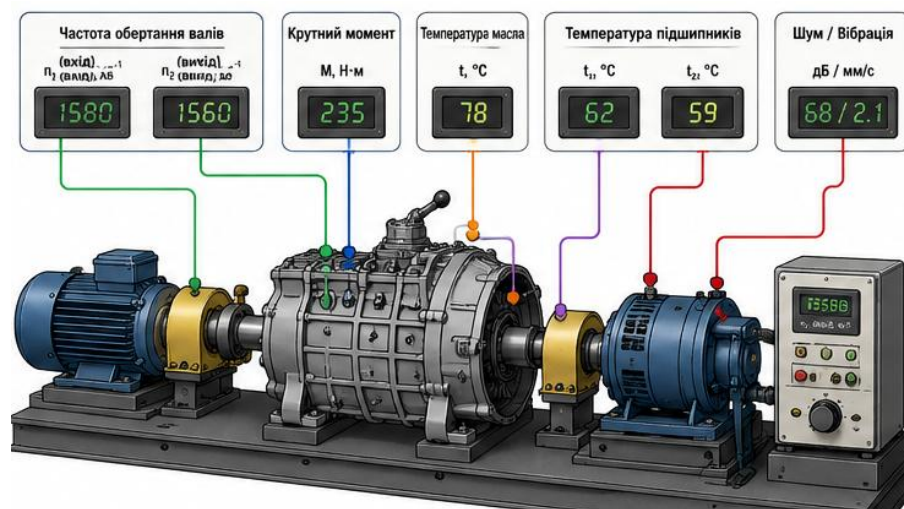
Контроль роботи КПП під час обкатування на стенді.
